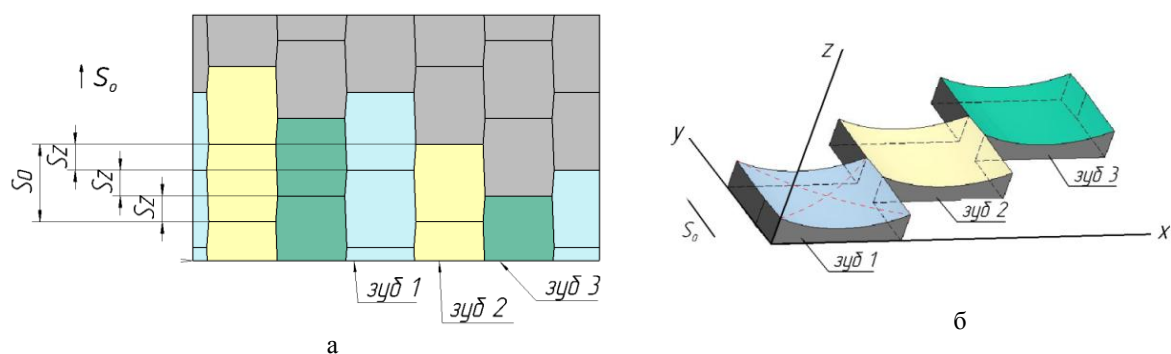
Вид поверхности (а) и ячеек (б), образованных трехзубой фрезой с режущей кромкой типа NR
